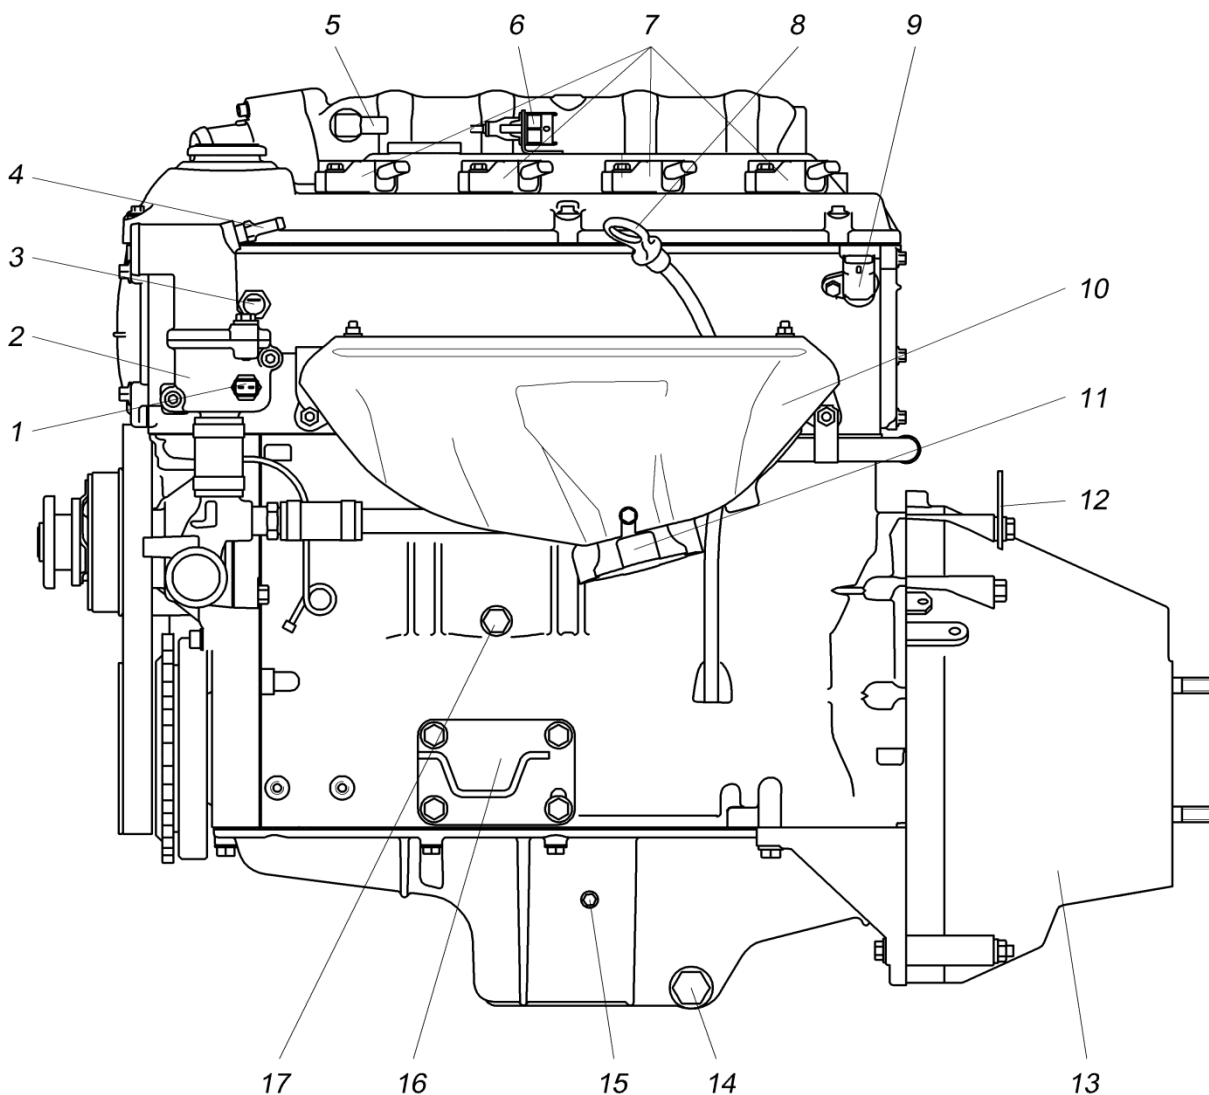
Левая сторона двигателя 3МЗ-40524.10 (экологического класса 3).
